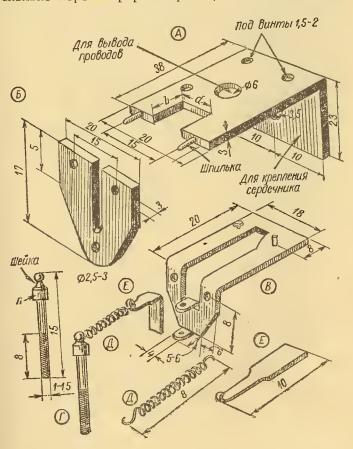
Детали электромагнитного реле типа 100: А — ярмо электромагнита: E — якорь; B — скоба; Γ — виат; \mathcal{I} — оттягивающая пружина; E — язычок для крепления оттягивающей пружины якоря,
